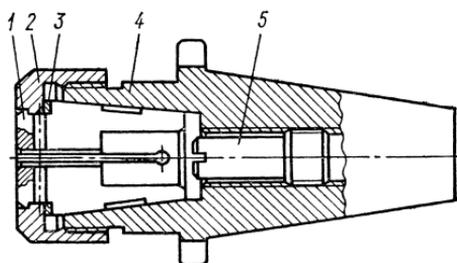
Цанговый патрон для крепления инструмента с цилиндрическим хвостовиком
